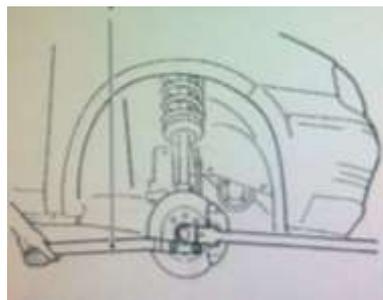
Montaje y Ajuste de la Tuerca de la Punta de Eje
